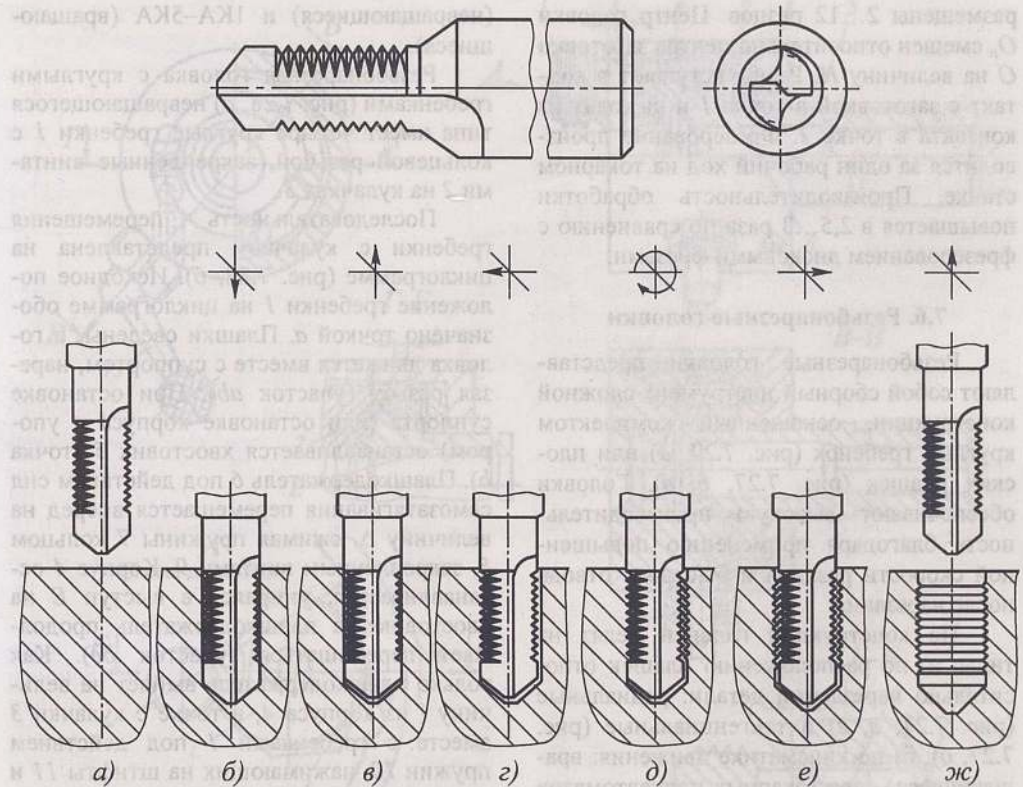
Схема обработки резьбового отверстия комбинированным резьбообразующим инструментом с планетарным движением (патент № 3627798, Германия)
